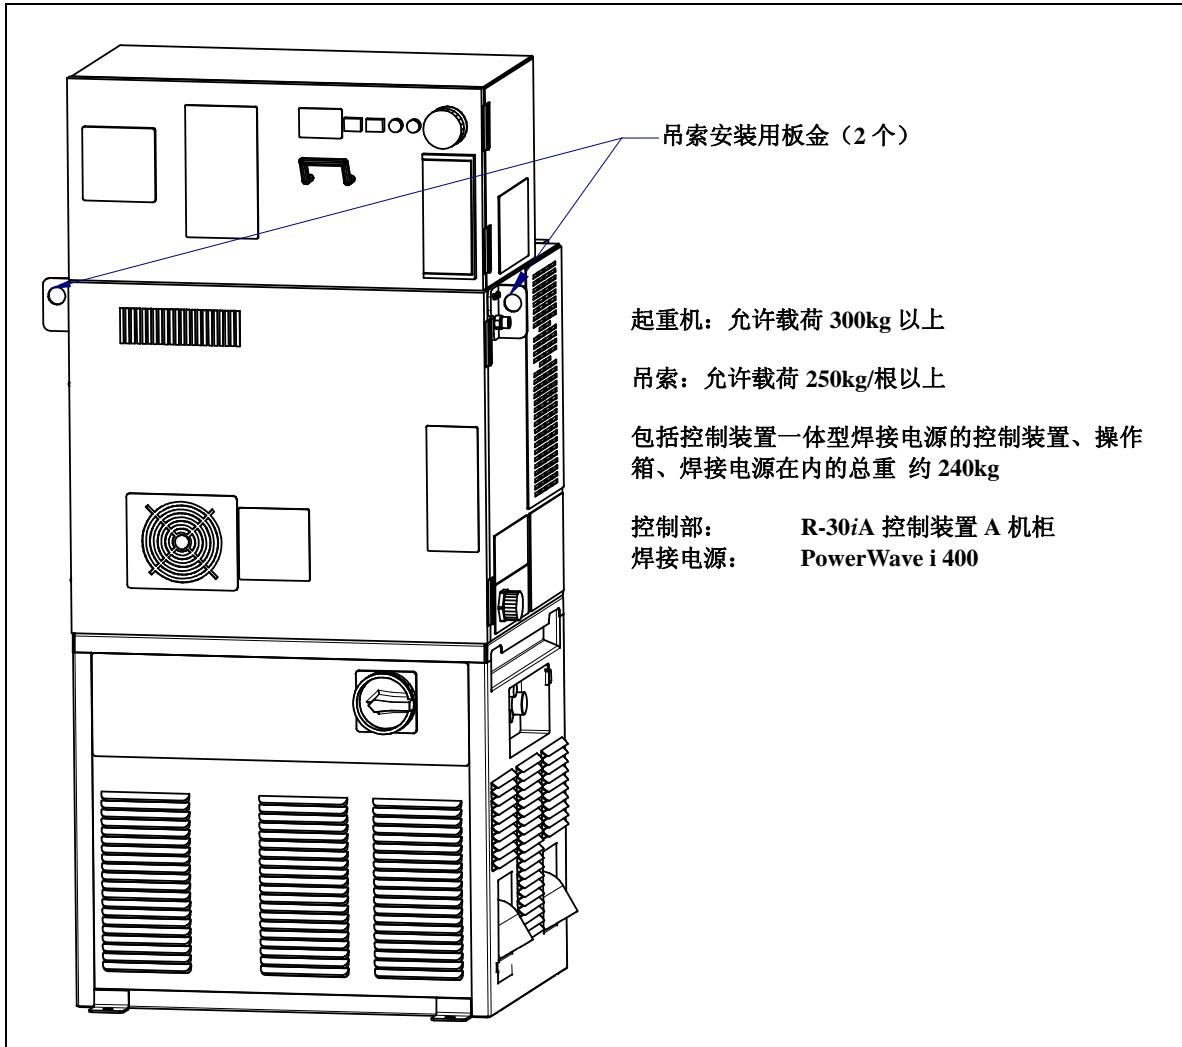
(d) 焊接电源一体型控制装置的搬运
